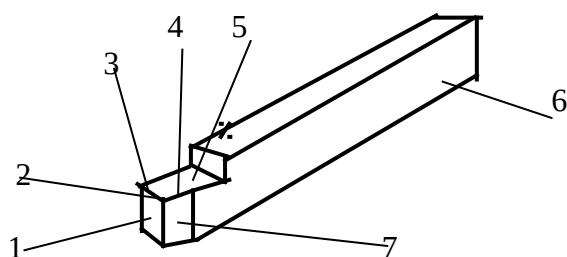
Элементы рабочей части (головки) токарного проходного резца:
